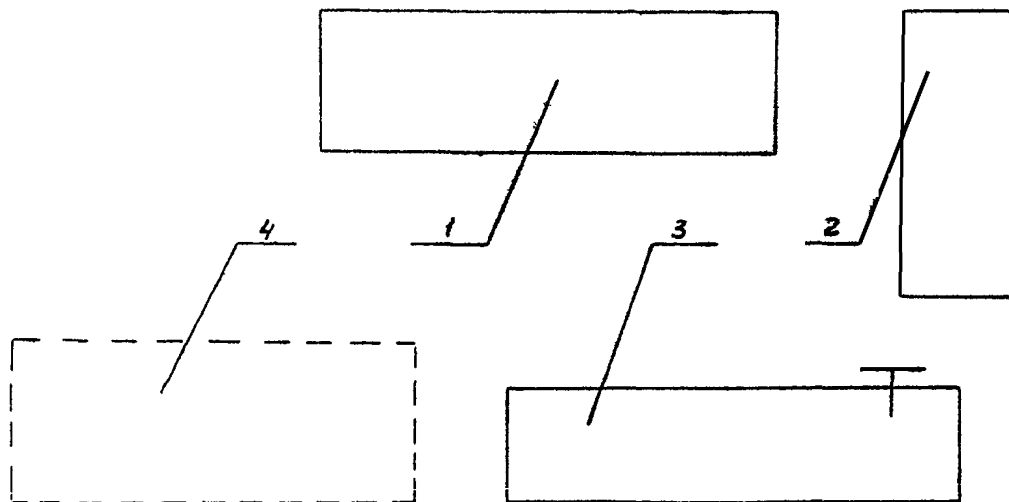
Типовая схема планировки рабочего места разборки и сборки механизма рулевого управления
